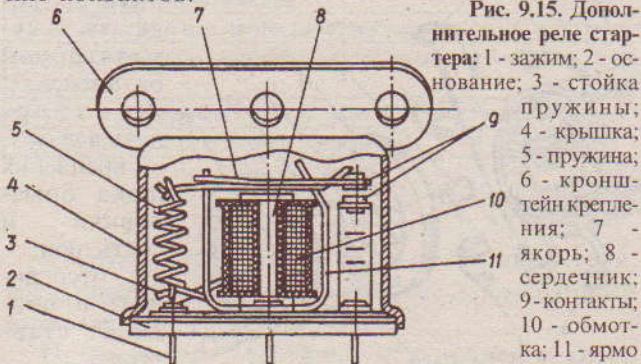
Дополнительное реле стартера: 1 - зажим; 2 - основание; 3 - стойка пружины; 4 - крышка; 5 - пружина; 6 - кронштейн крепления; 7 - якорь; 8 - сердечник; 9 - контакты; 10 - обмотка; 11 - ярмо
